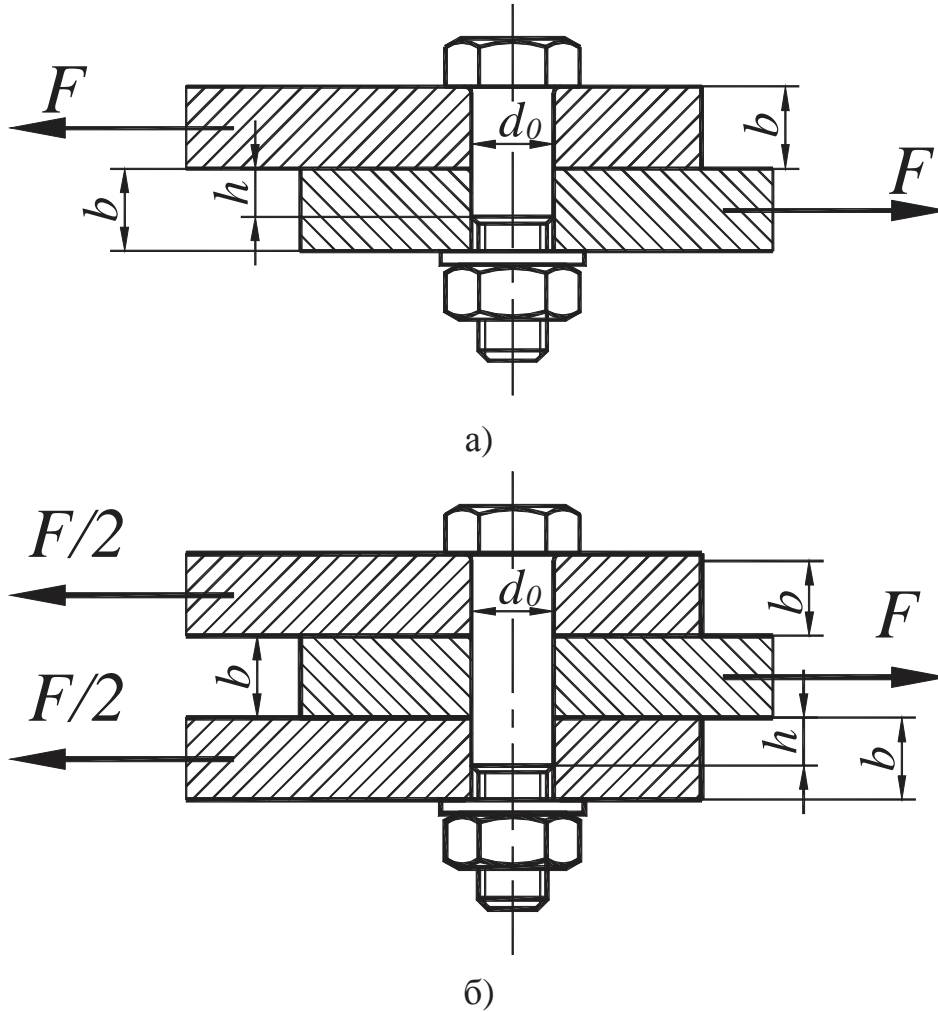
Розрахункова схема болтового з'єднання без зазору
